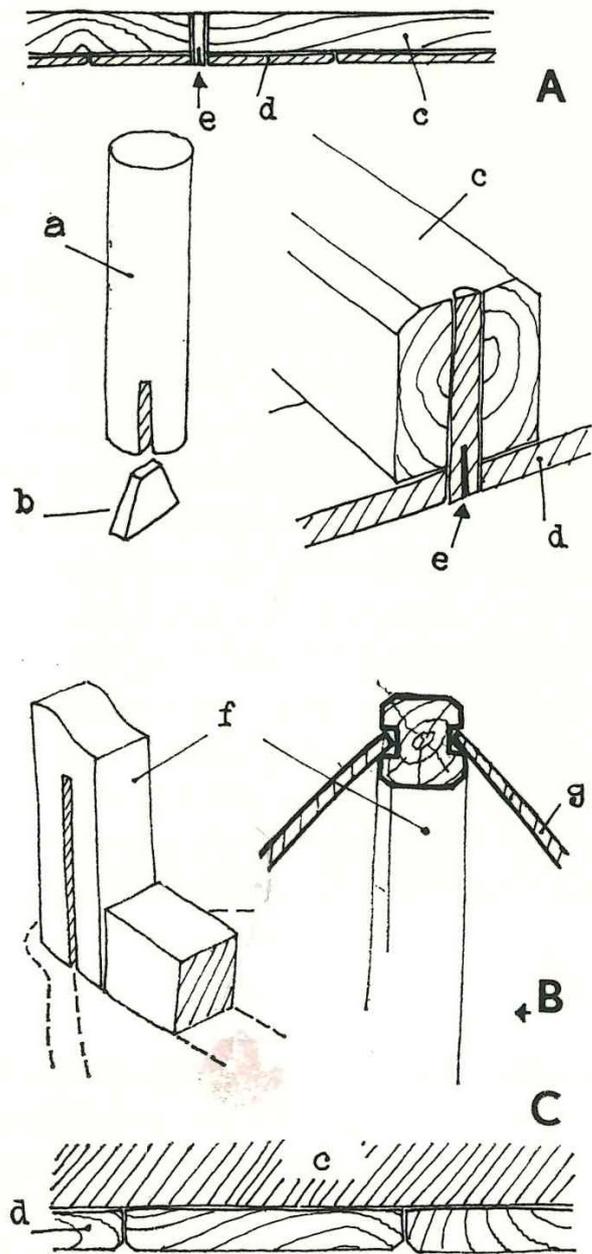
Pormenores de construção da barca de passageiros: A—processo de fixação das tábuas do fundo às cavernas; B—processo de ligação dos lados à proa; C—as tábuas do fundo, encostam-se umas às outras sem haver sobreposição. • a—cavilha; b—cunha; c—caverna; d—tábua do fundo; e—cavilha e cunha; f—proa; g—lados.
